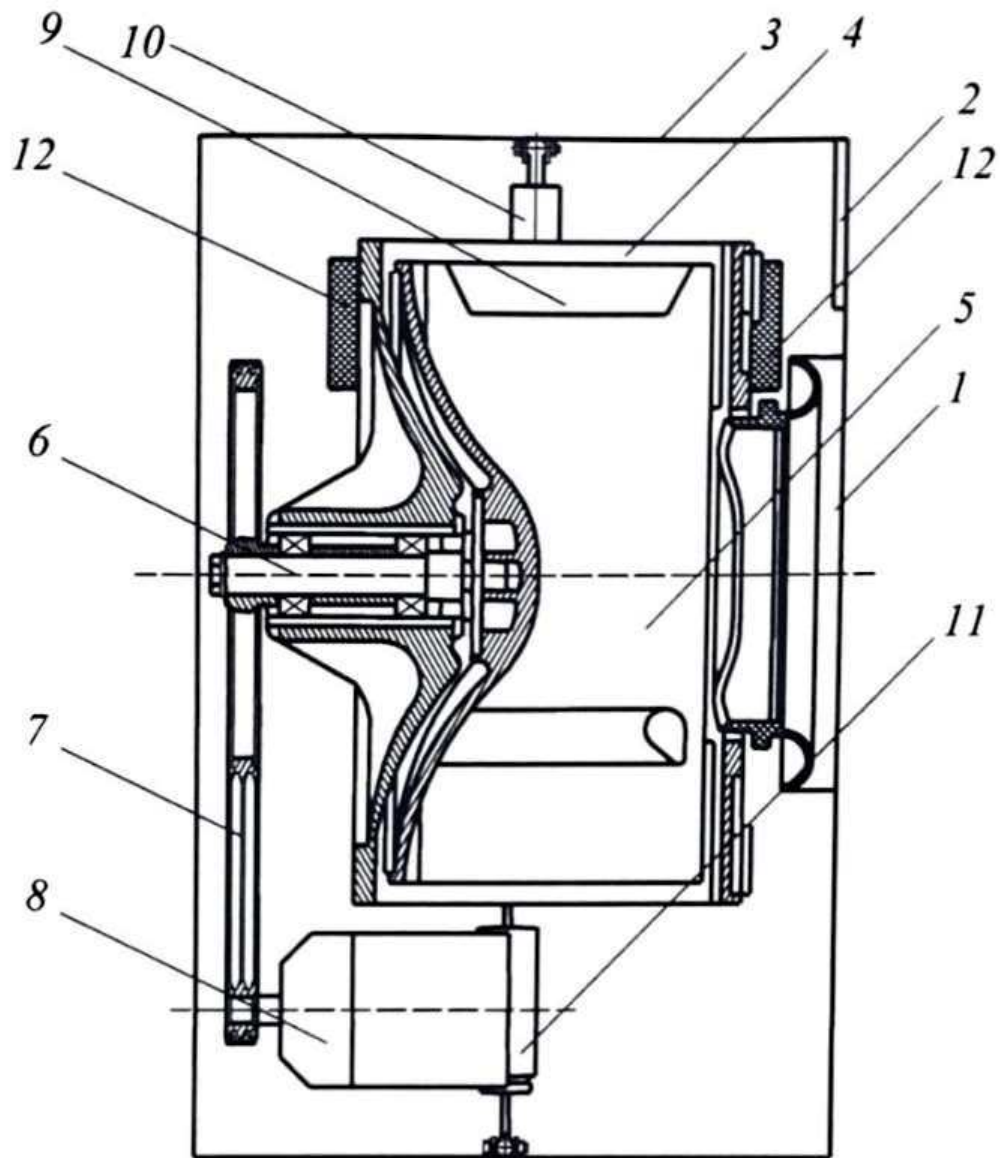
Пральна машина Samsung: 1 - люк для завантаження білизни; 2 - панель керування; 3 – корпус машини; 4 – бак; 5 – барабан для білизни; 6 - вал; 7 - передача пасова; 8 - електродвигун; 9 - гребінь; 10 - демпфер пружинний; 11 - демпфер гідравлічний
